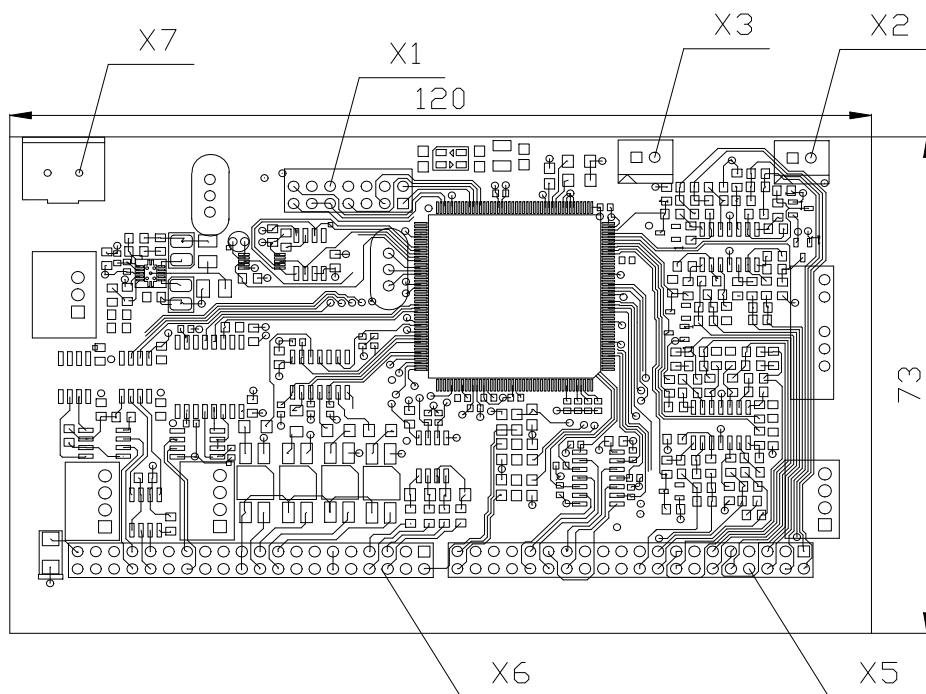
Габаритные и присоединительные размеры платы контроллера МК20.3
